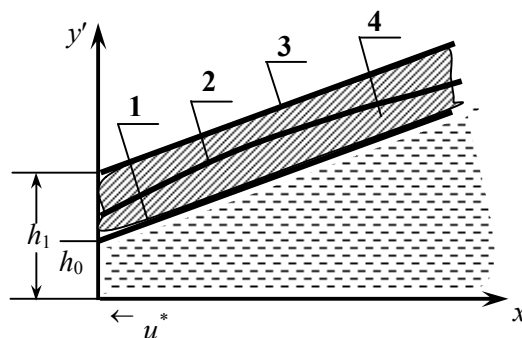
Схематическое изображение упорного подшипника: 1 – недеформированный контур, прилегающий к смазочному слою; 2 – деформированный контур; 3 – недеформированный контур, прилегающий к жесткой опорной поверхности подшипника; 4 – упругий слой
